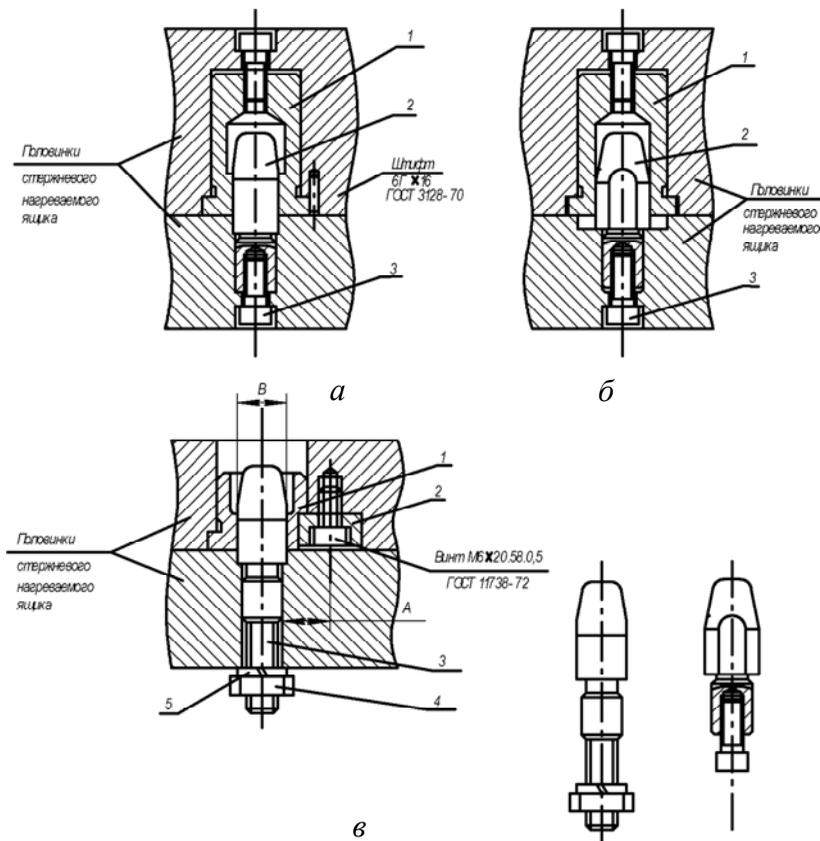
Примеры центрирующих соединений полуформ нагреваемых стержневых ящиков:
